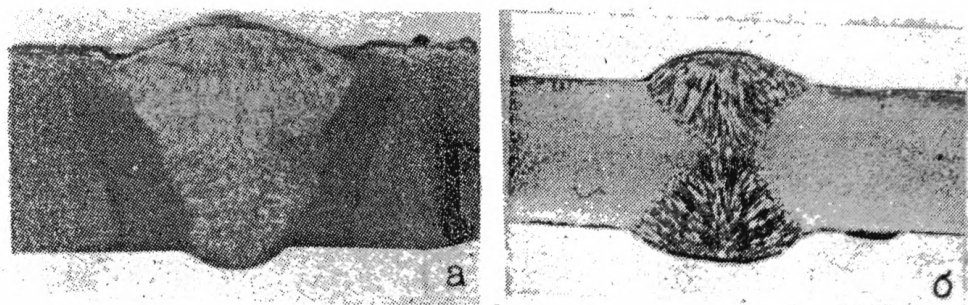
Стыковое соединение, выполненное сваркой:
